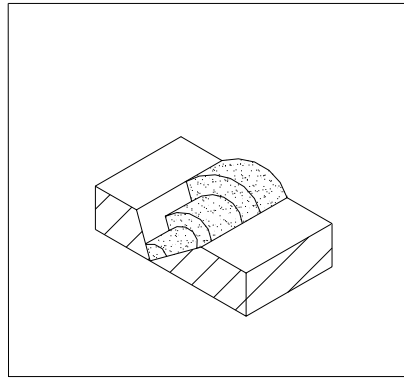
PASADAS EN SOLDADURA
